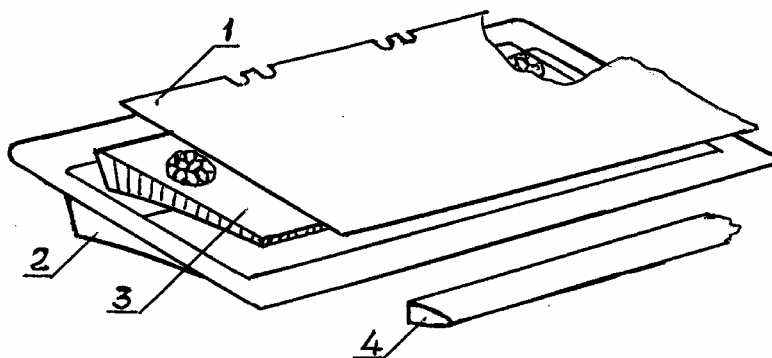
Интерцептор интегральной конструкции: 1 – обшивка верхняя; 2 – чашка; 3 – сотоблок; 4 – законцовка
